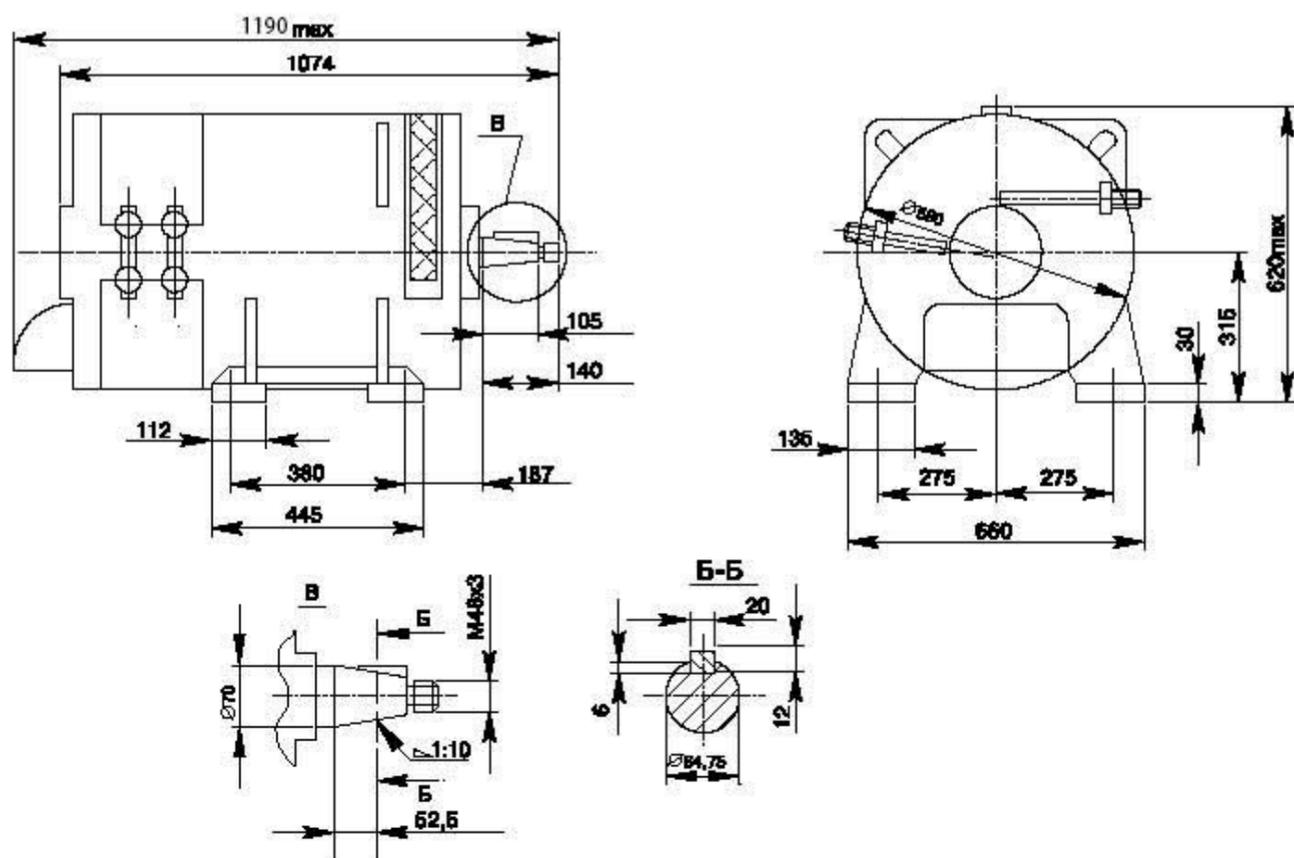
Габаритные и установочные размеры стартер-генератора СПСГМ
